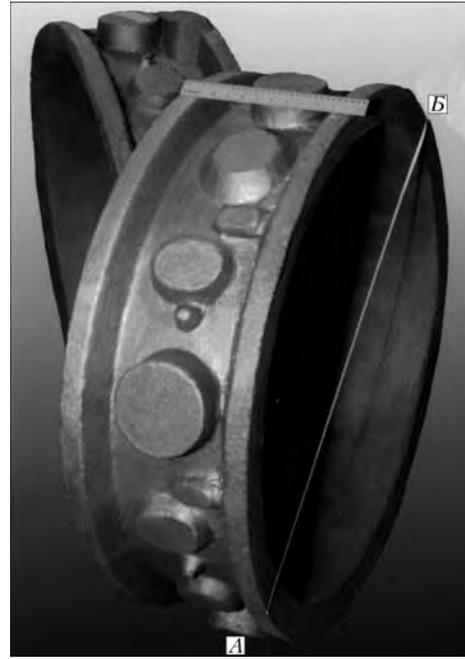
Отливки ЦЭШЛ из стали ЭП 517
